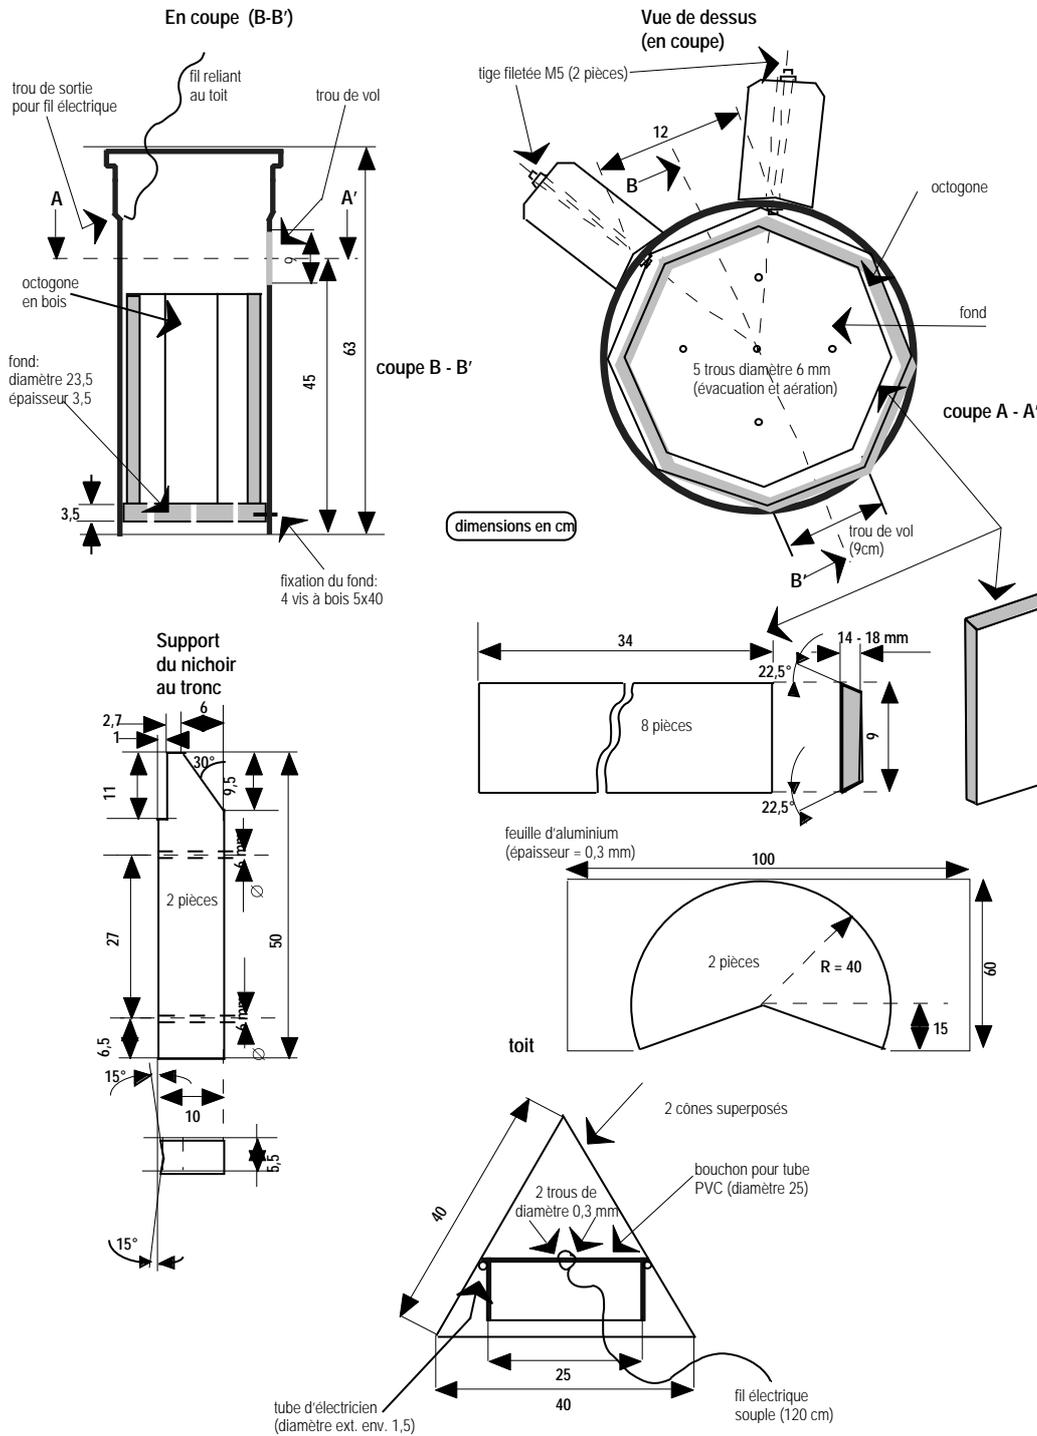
Plan de fabrication du nichoir de type «tube PVC».
